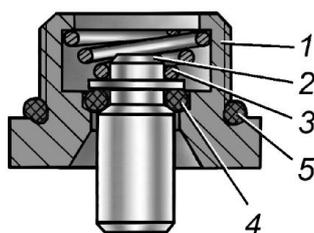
Кран слива конденсата: 1 - корпус; 2 - толкатель; 3 - пружина; 4, 5 - кольцо.
